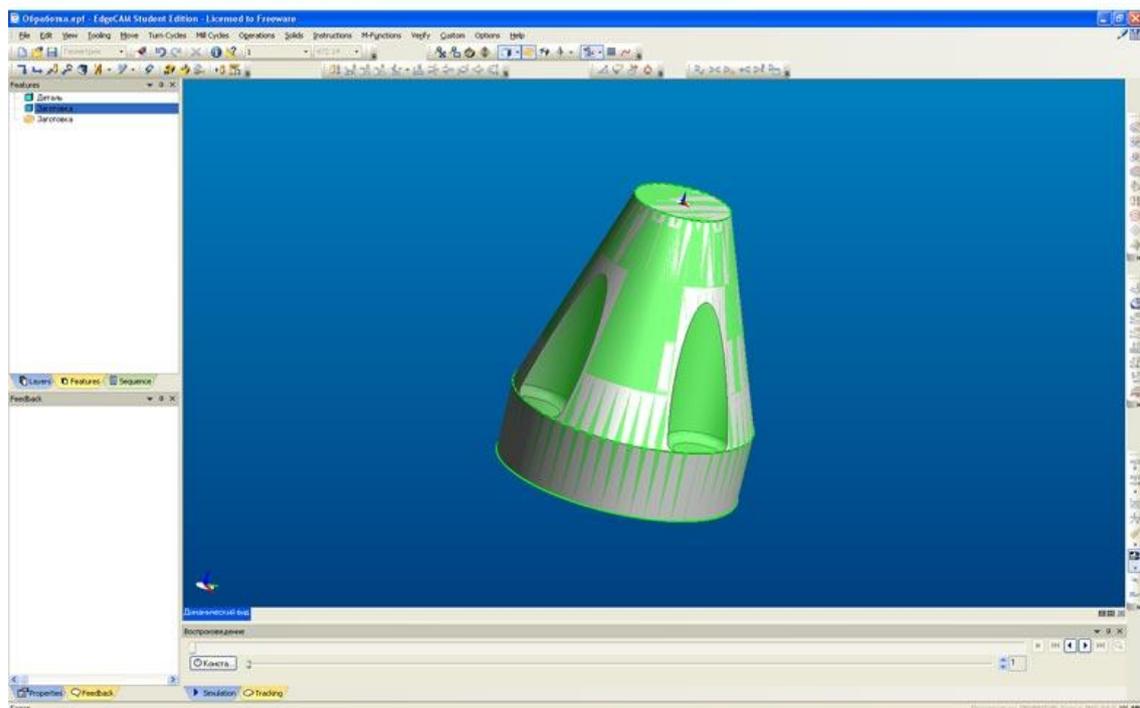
Edgesam. Заготовка была создана с учётом токарной обработки
